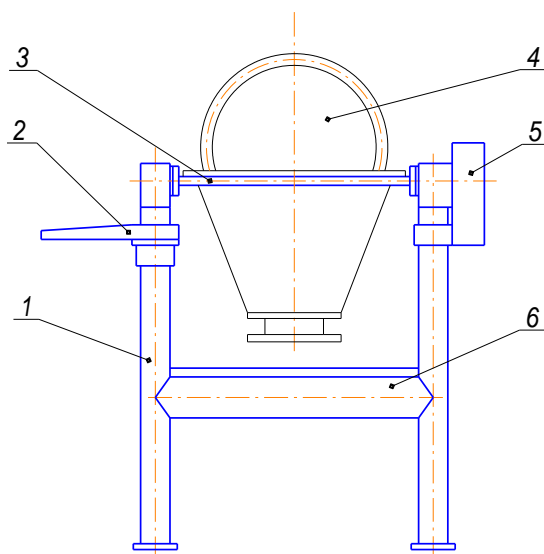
Стенд для разборки и сборки редукторов задних мостов Р-236:
